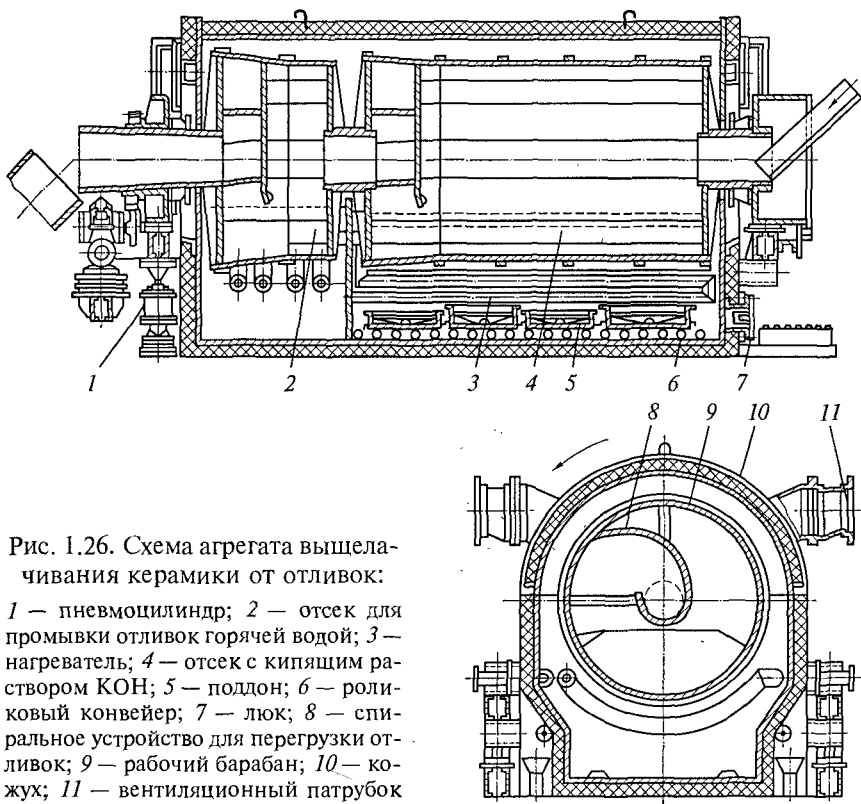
Схема агрегата выщелачивания керамики от отливок:
